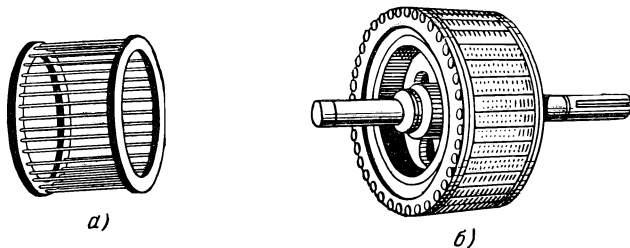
Обмотка типа «беличье колесо» (*а*) и коротко замкнутый ротор (*б*).
